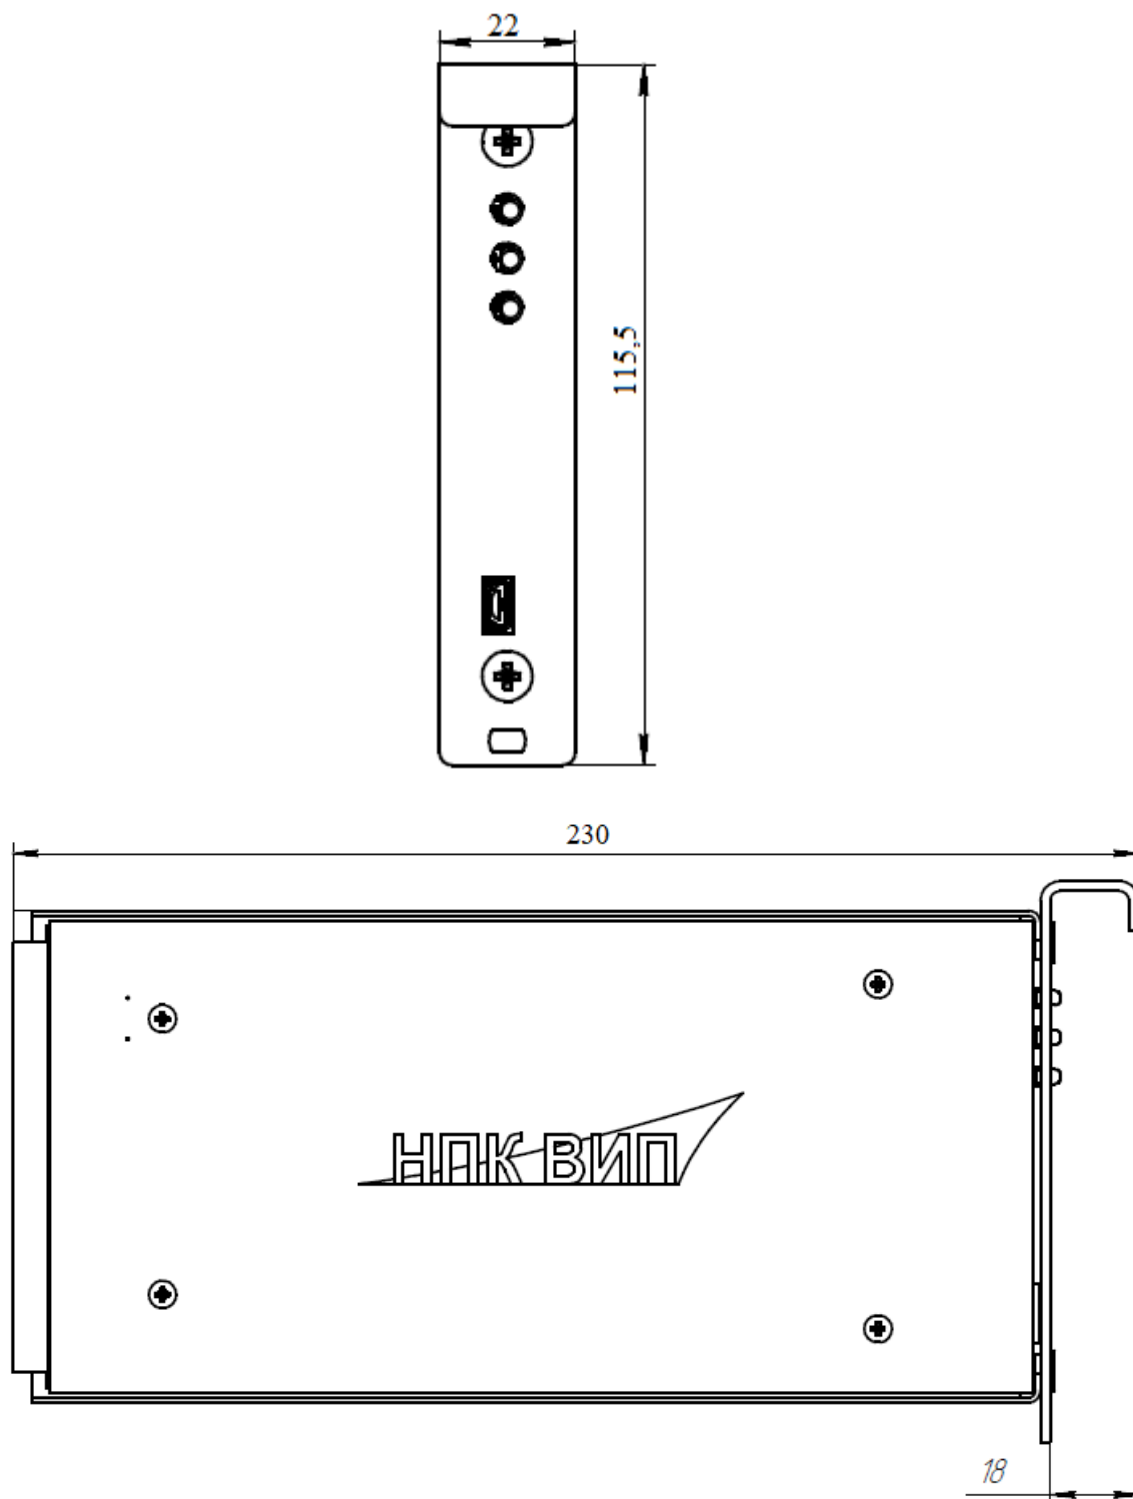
Внешний вид и справочные габаритные размеры контроллера
